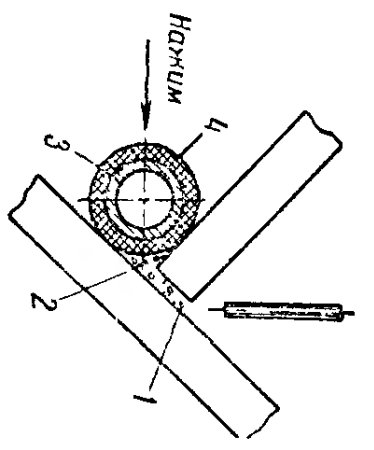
Сварка угловых швов при увеличенном зазоре
